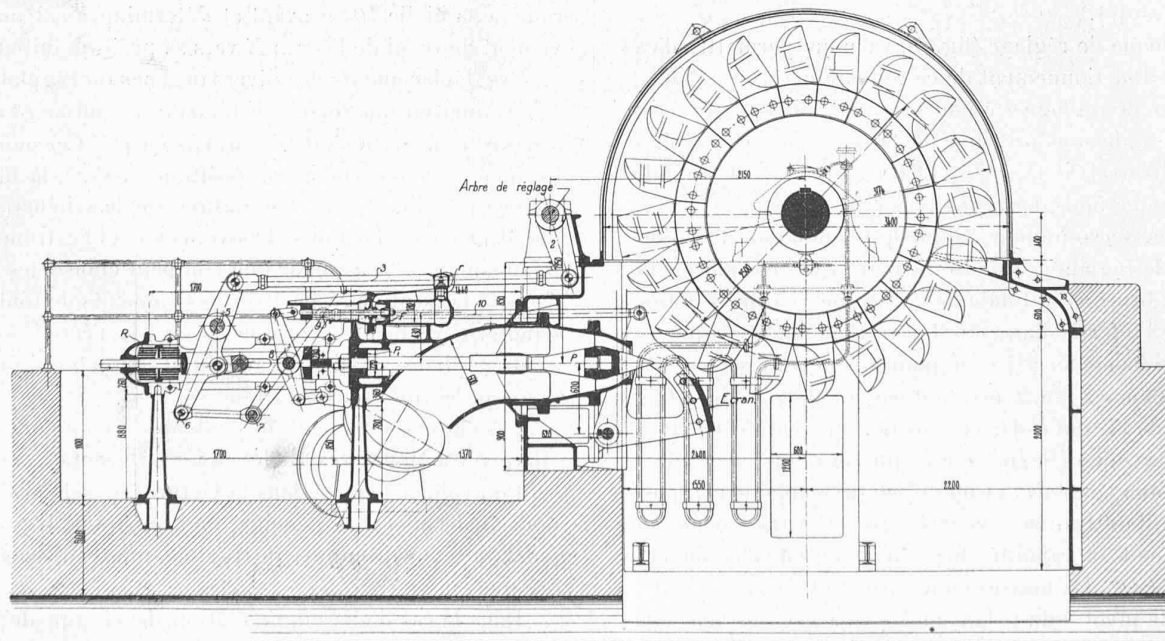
Turbine Pelton, de la Borgne: Coupe par le distributeur. — 1 : 60.
